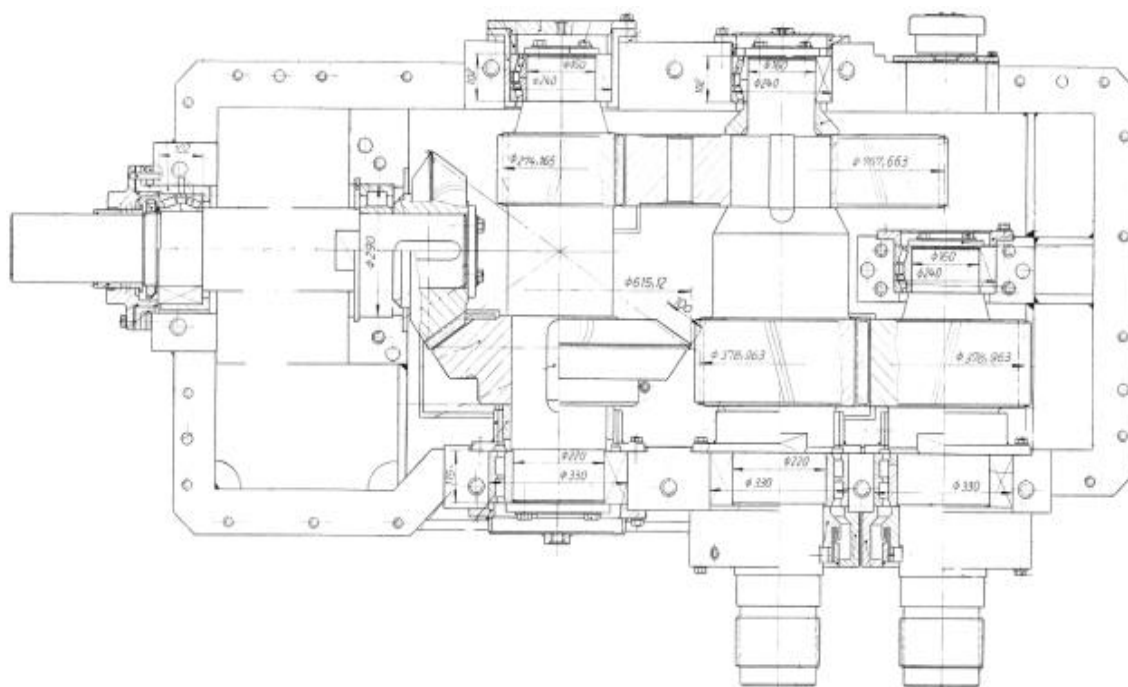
Разрез комбинированного шестерённого редуктора прокатной клетки с вертикальным расположением валков
